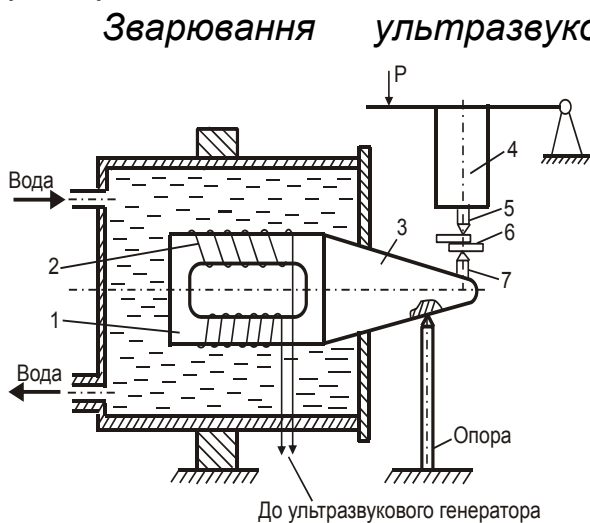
Схема установки для точкового зварювання ультразвуком
